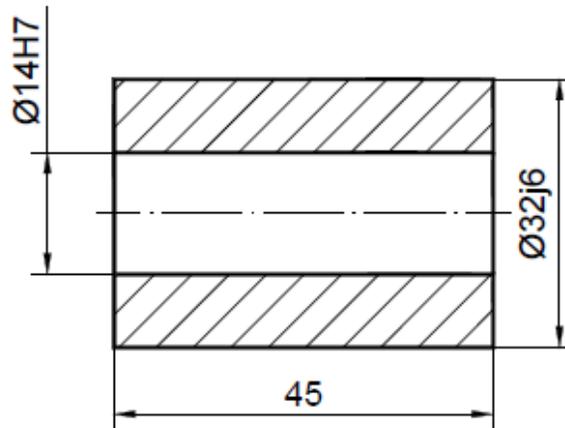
Indicación de la tolerancia dimensional en forma codificada.
